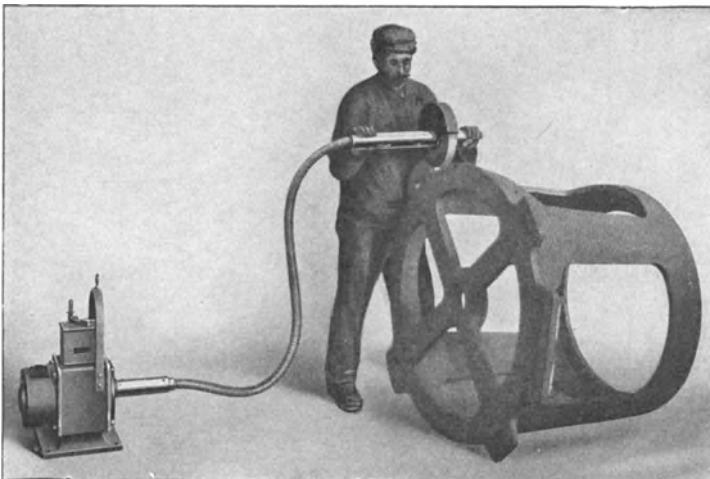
Handschleifmaschine mit biegsamer Welle.
